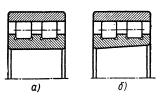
Роликоподшипники с короткими цилиндрическими роликами радиальные духрядные, ГОСТ 7634—56: a-c цилиндрическим отверстием; $\delta-c$ коническим отверстием (конусность 1:12)
